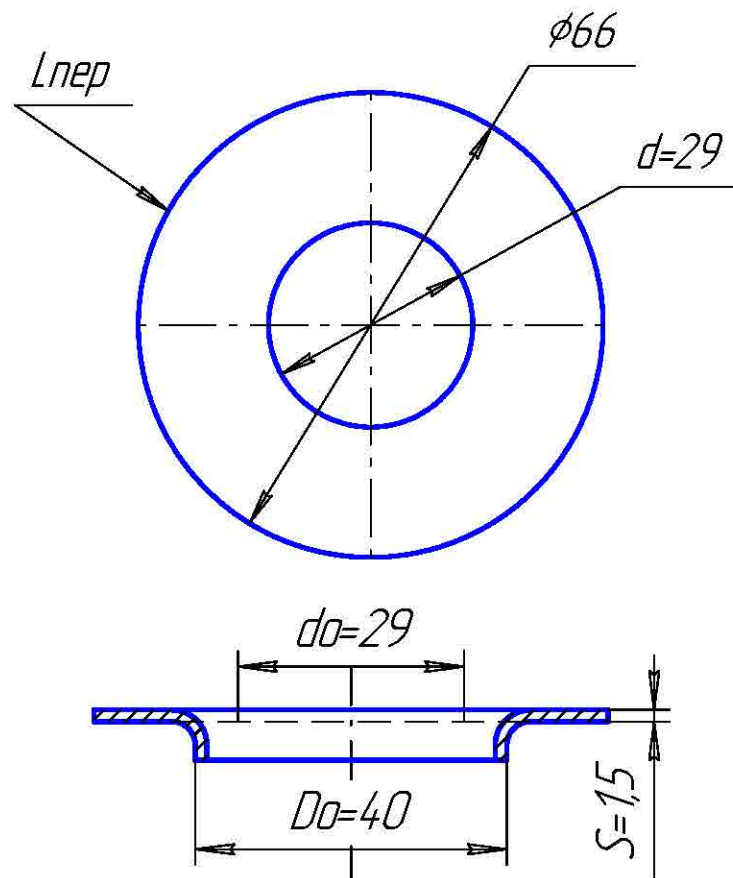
Ескізи заготовки та деталі по операціям.
